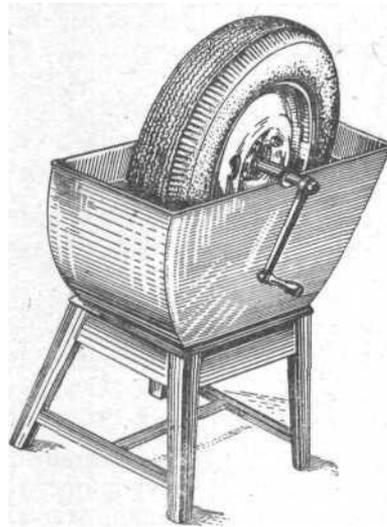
Ванна для проверки герметичности соединения обода колеса с диском
